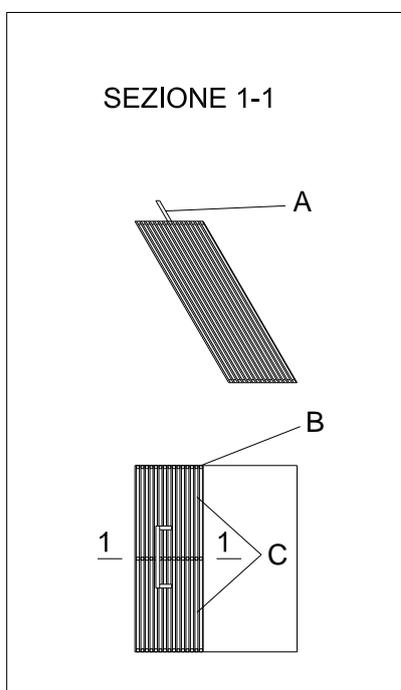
pacchetto lamellare, A) Maniglie, B) Distanziatori, C) Pacchetto filtrante lamellare
